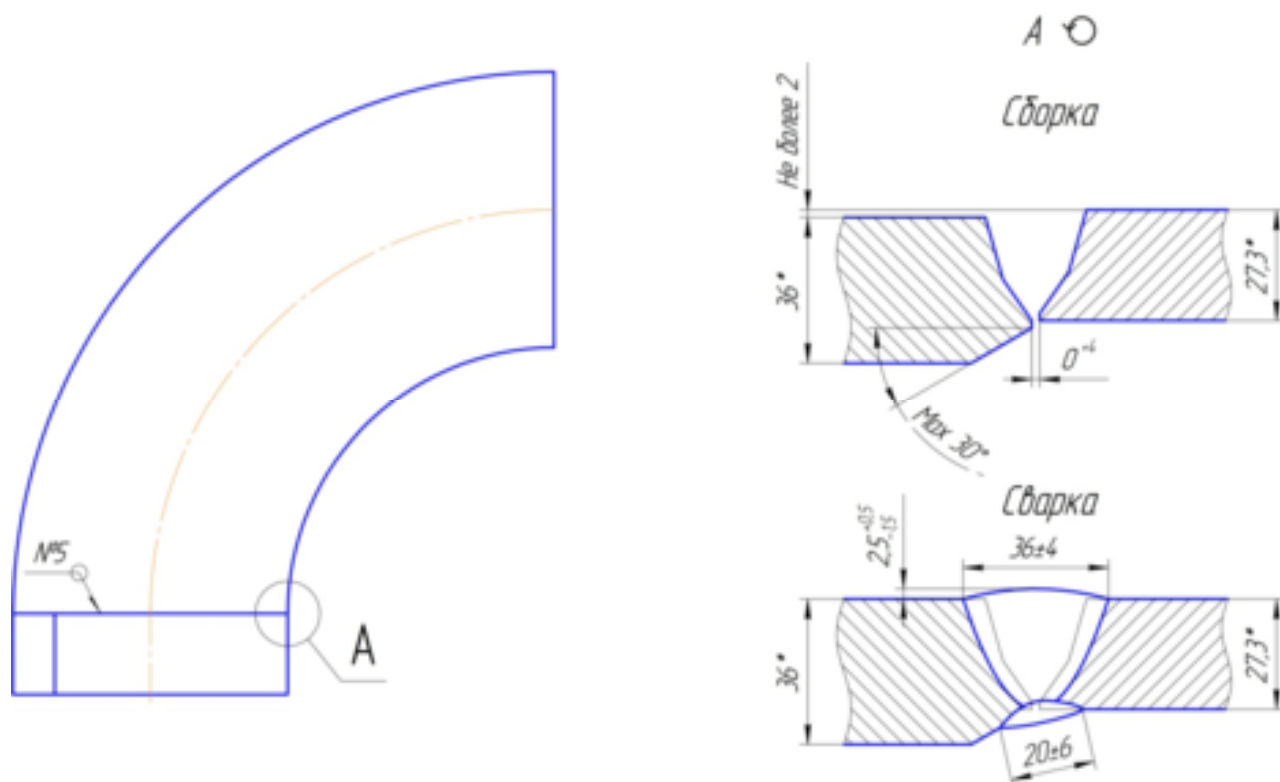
Схема сборки и сварки отвода с кольцом
